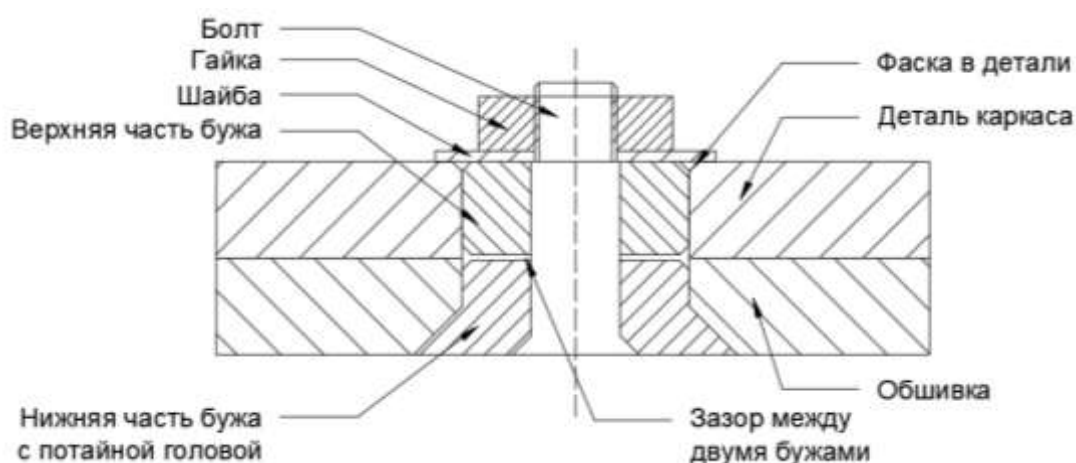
Схема установки ремонтных втулок (бужей) в пакет деталей
